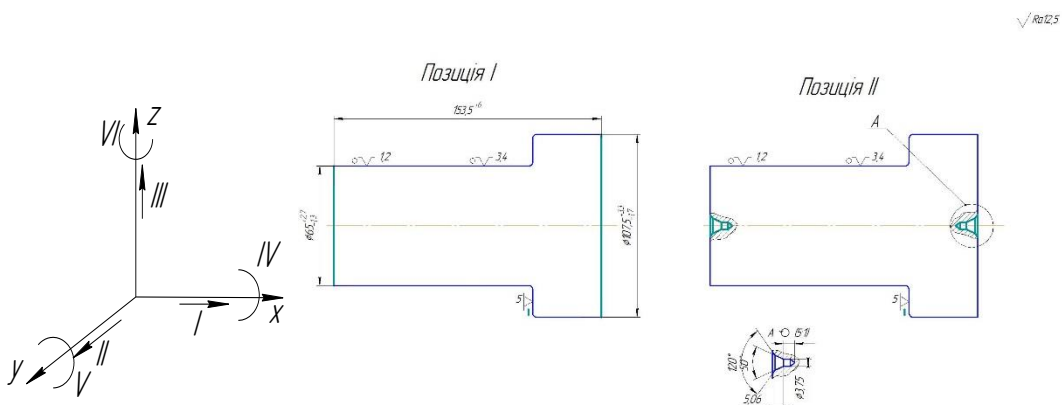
Схема базування заготовки на фрезерно-центрувальній операції
